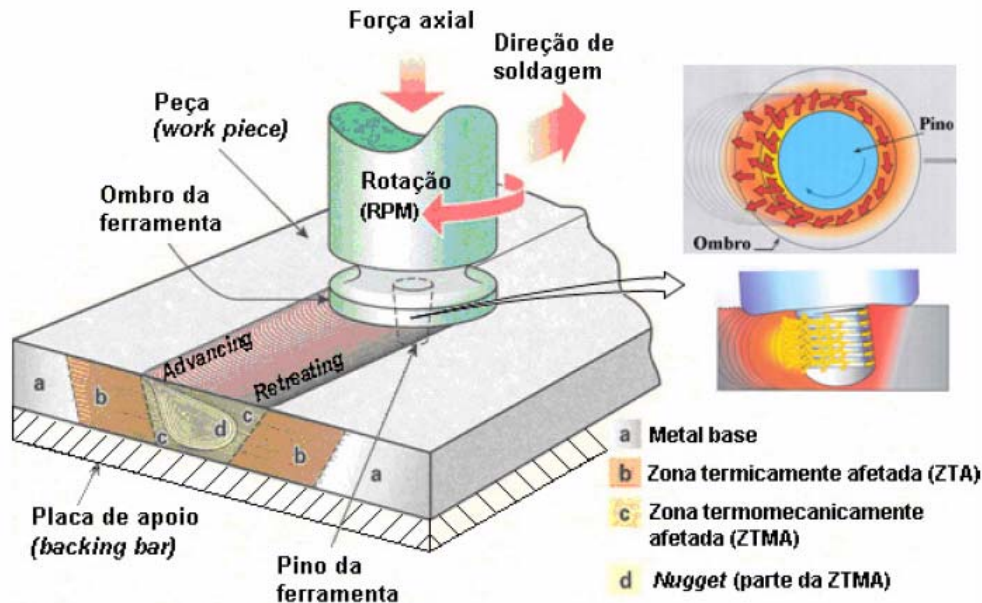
processo de soldagem por FSW – Friction Stir Welding. Fonte: CRUZ e NETO, 2009 P.6.
